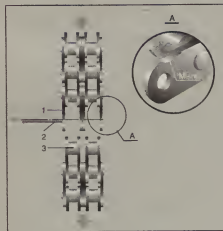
Расстыковка цепи: 1 — пластина; 2 — палец; 3 — втулка. "А" — метка (фаска).
